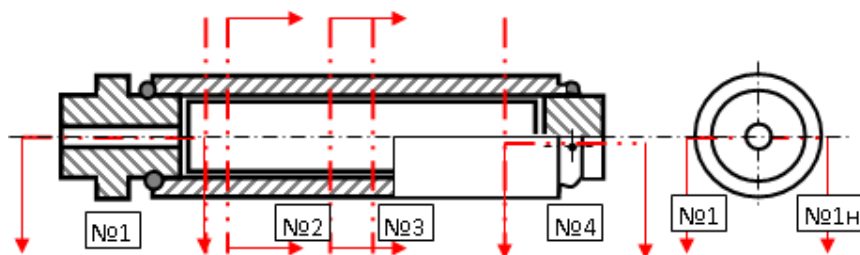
Схема разрезки разгерметизировавшихся трубчатых образцов № 1, 4 – шлифы в продольном сечении; № 2, 3 – шлифы в поперечном сечении
